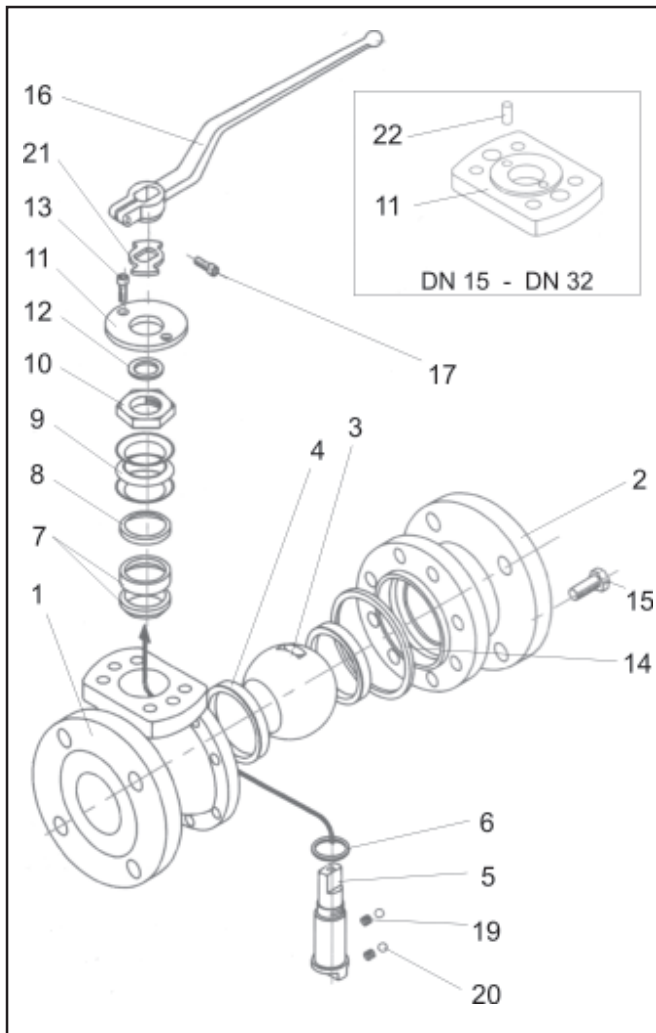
Explosionszeichnung des Kugelhahns BR 76a
